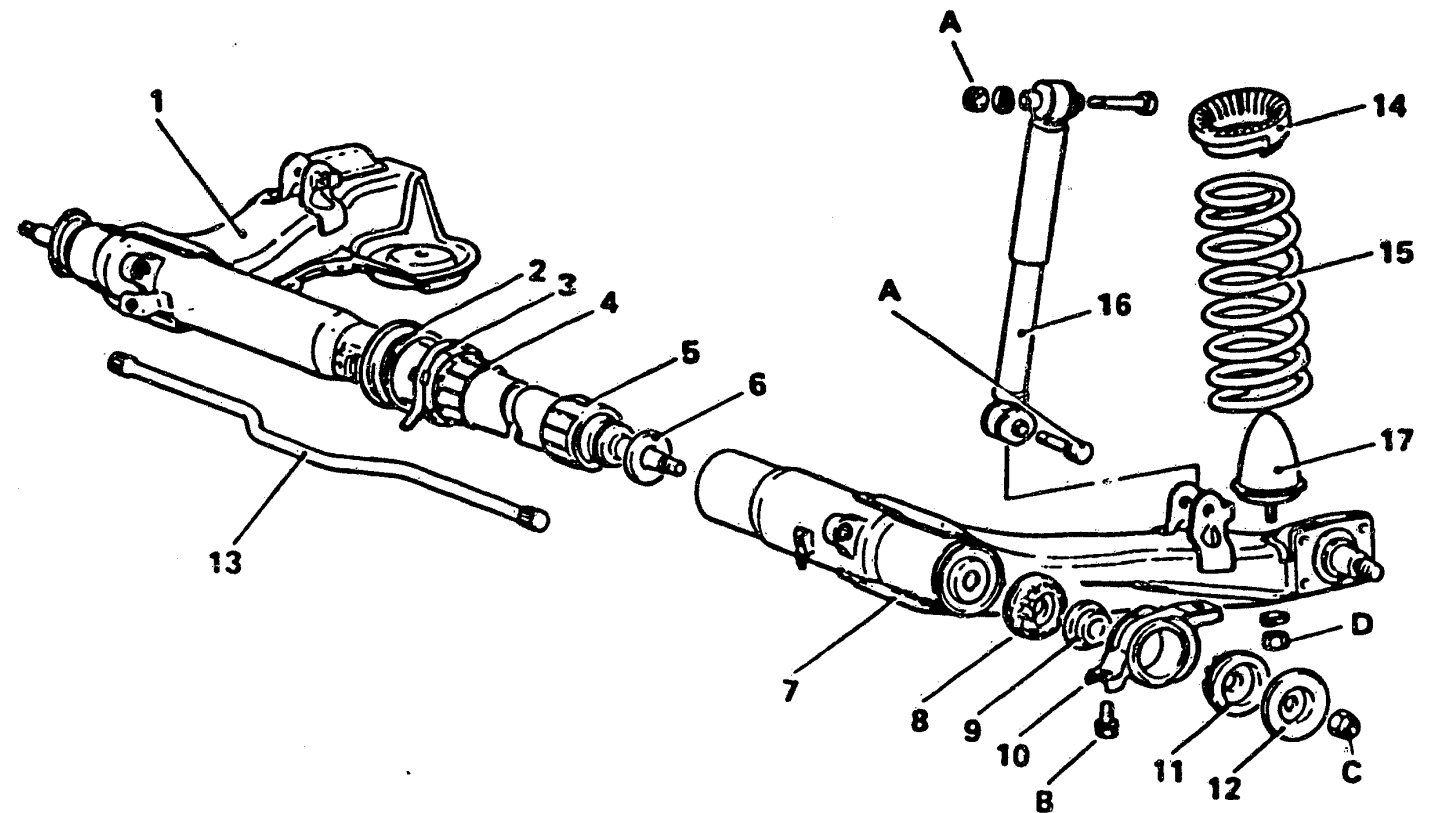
Einzelteile der Hinterradaufhängung: 1 Rechter Längslenker – 2 Staubschutz – 3 Klemme – 4 Büchse A – 5 Büchse B – 6 Gummianschlag – 7 Linker Längslenker – 8 Gummibüchse (innen) – 9 Gummianschlag – 10 Befestigung – 11 Gummibüchse (ausen) – 12 Scheibe – 13 Stabilisator – 14 Federsitz – 15 Schraubenfeder – 16 Stossdämpfer – 17 Anschlag.
